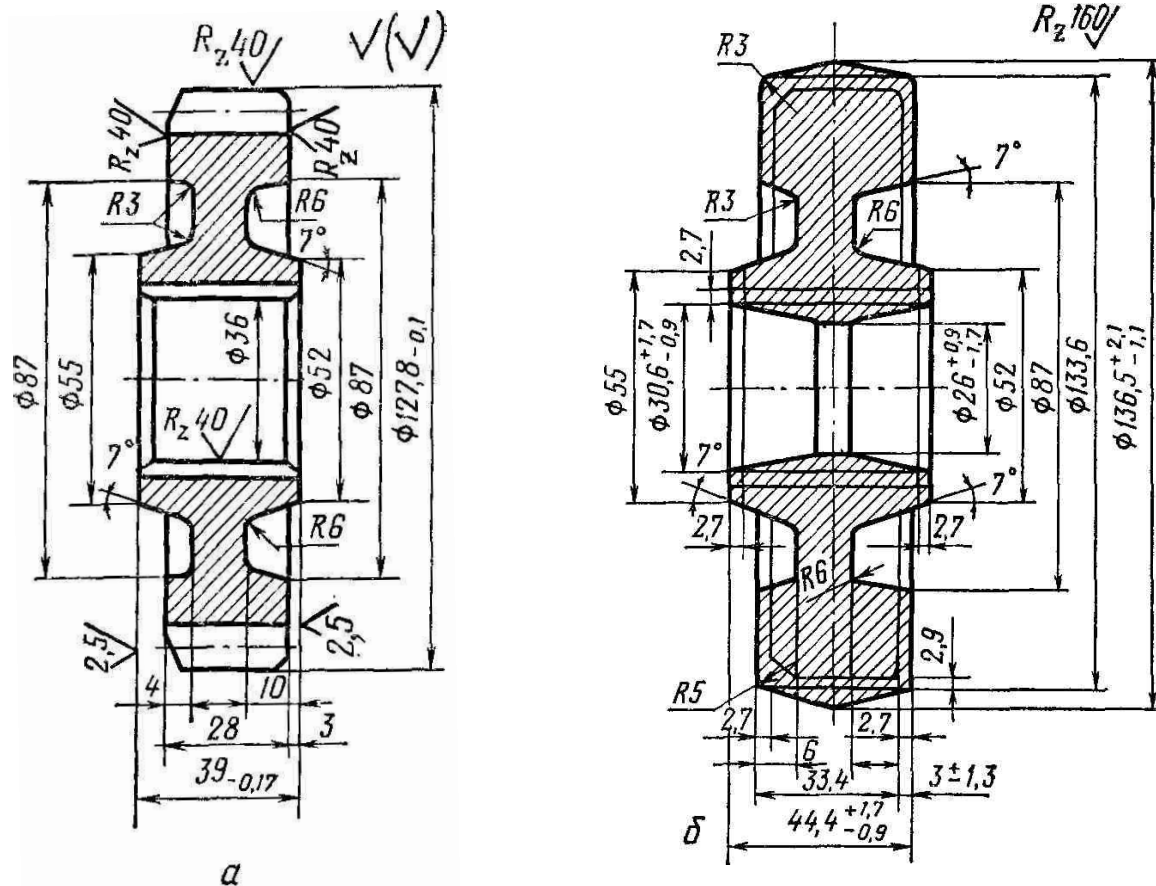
Цилиндрическое зубчатое колесо трактора:
